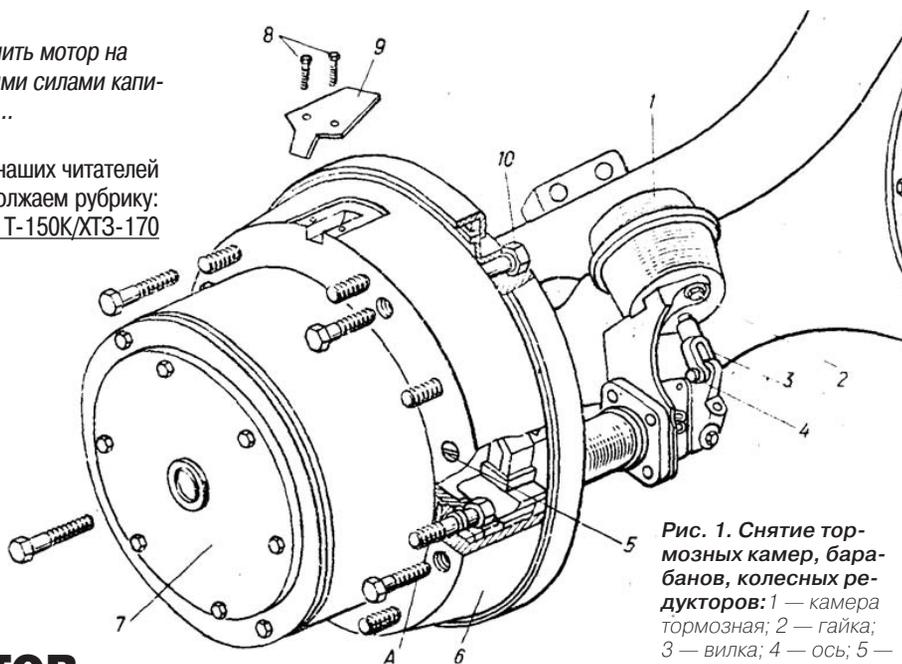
Снятие тормозных камер, барабанов, колесных редукторов: 1 — камера тормозная; 2 — гайка; 3 — вилка; 4 — ось; 5 — винт; 6 — барабан; 7 — редуктор; 8, 10 — болт; 9 — крышка; А — болт технологический
